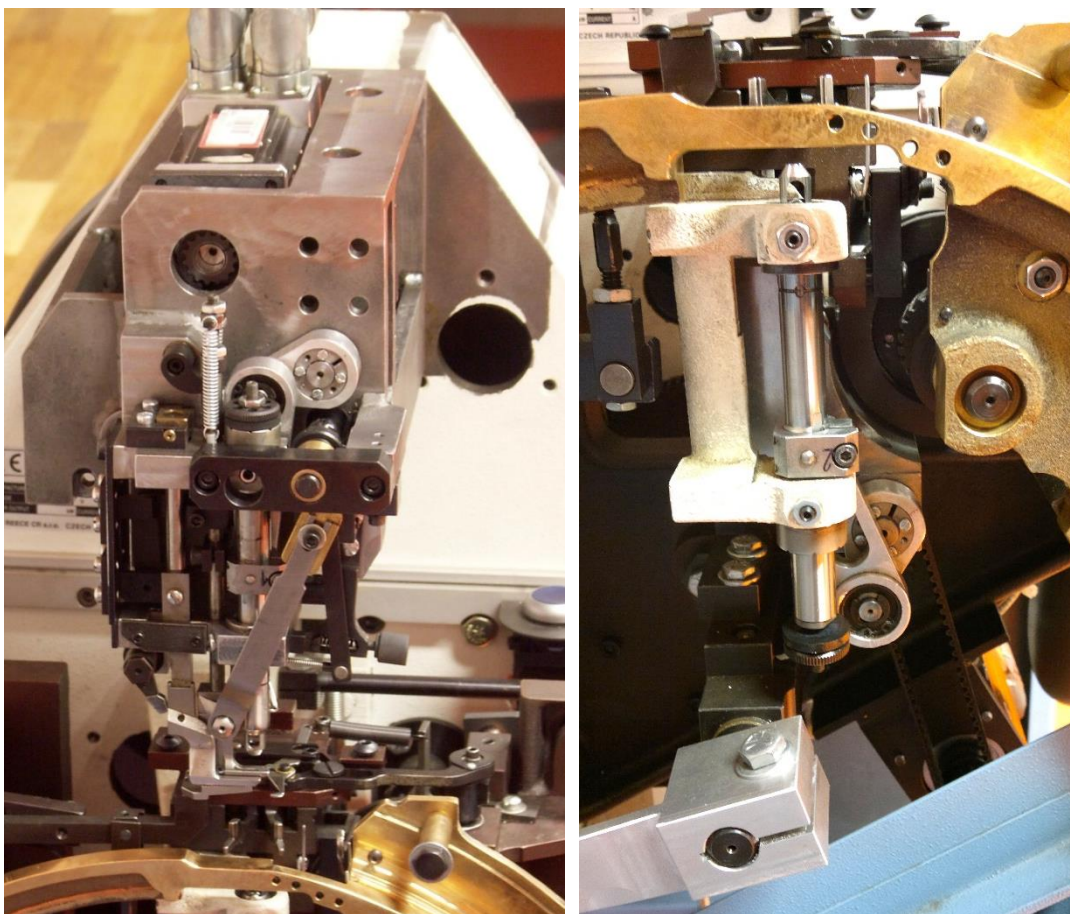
Implementace mechanismu jehelních týčů do šicího stroje
